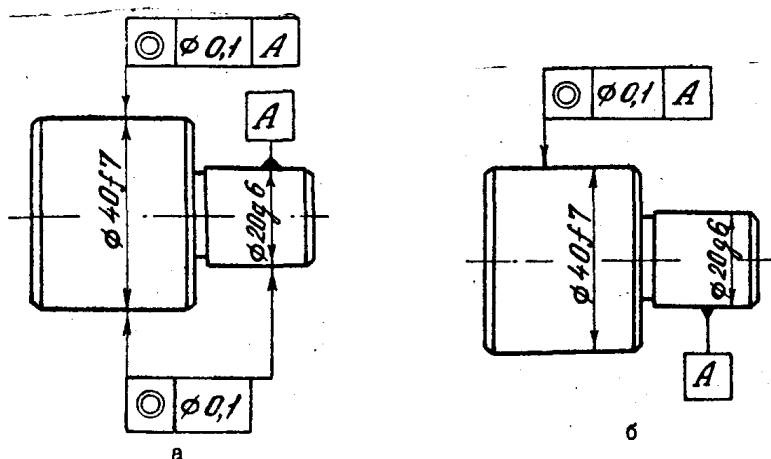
Позначення допуску форми чи розміщення поверхонь на кресленні
